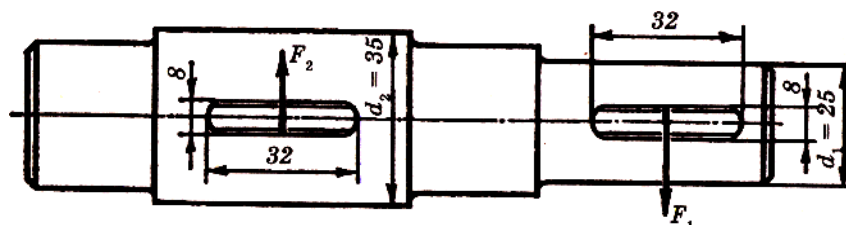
Ступенчатый вал с одинаковыми шпонками
